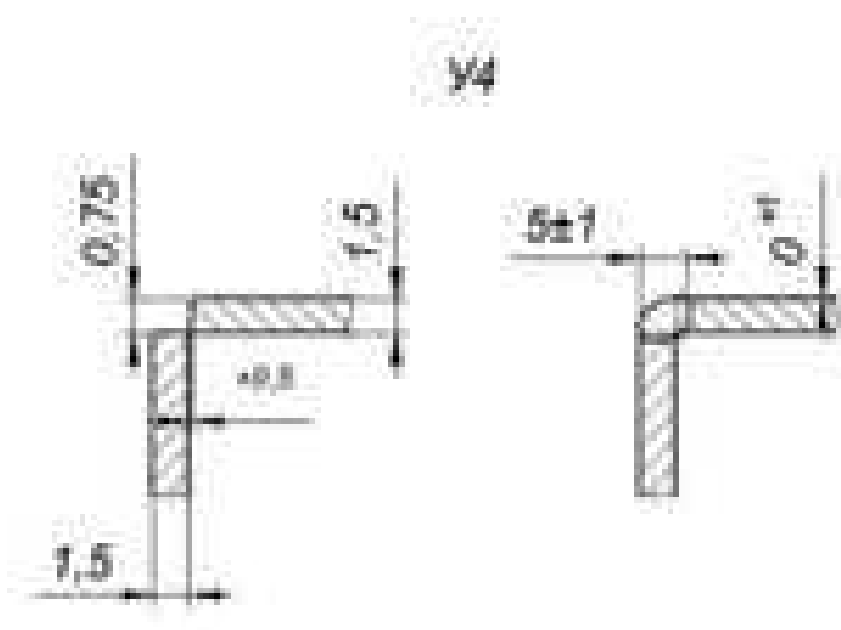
Эскиз углового сварного шва
